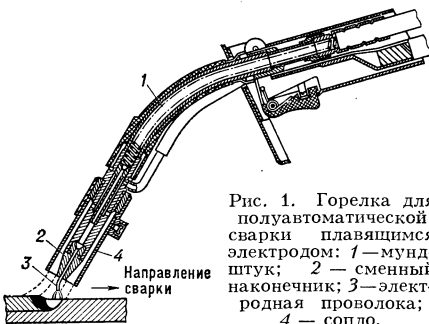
Горелка для полуавтоматической сварки плавящимся электродом: 1 — мундштук; 2 — сменный наконечник; 3 — электродная проволока; 4 — сопло.
